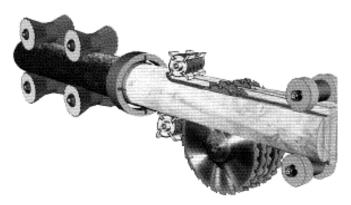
Схема работы фрезерно-профилирующего агрегата
